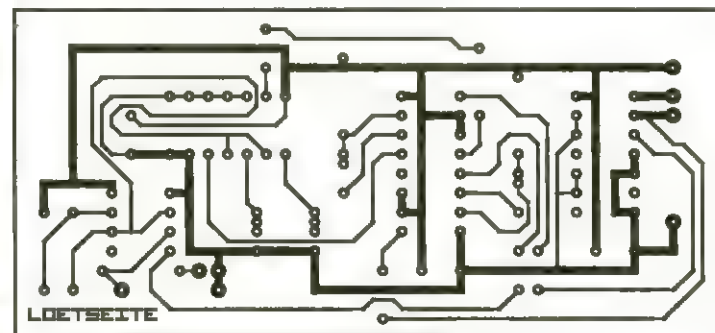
Wer es gerne edel mag, kann statt einer Lochrasterplatte auch eine Platine ätzen. Hier sind Layout...
